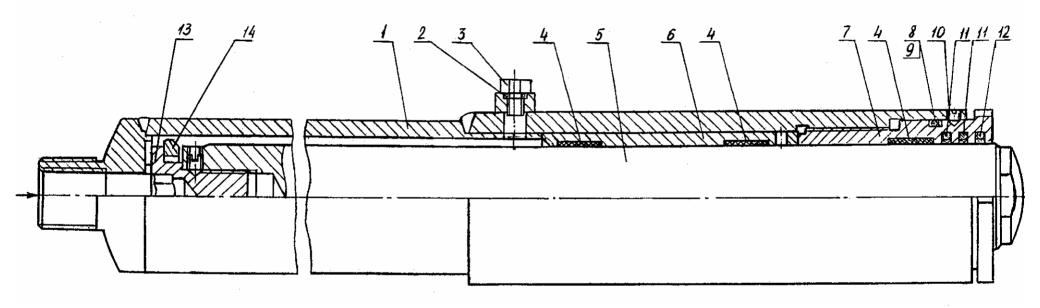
Гидроцилиндр подъема Fig. 3 Rise Hydraulic Cylinder
